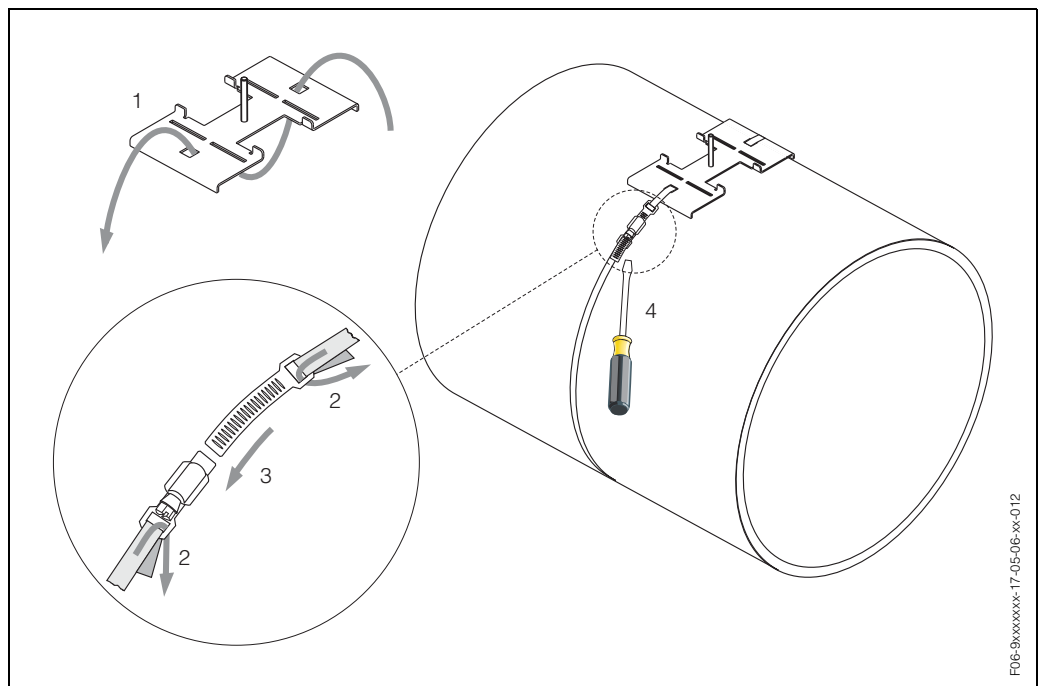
Installazione delle fascette di fissaggio per DN 250...4000
